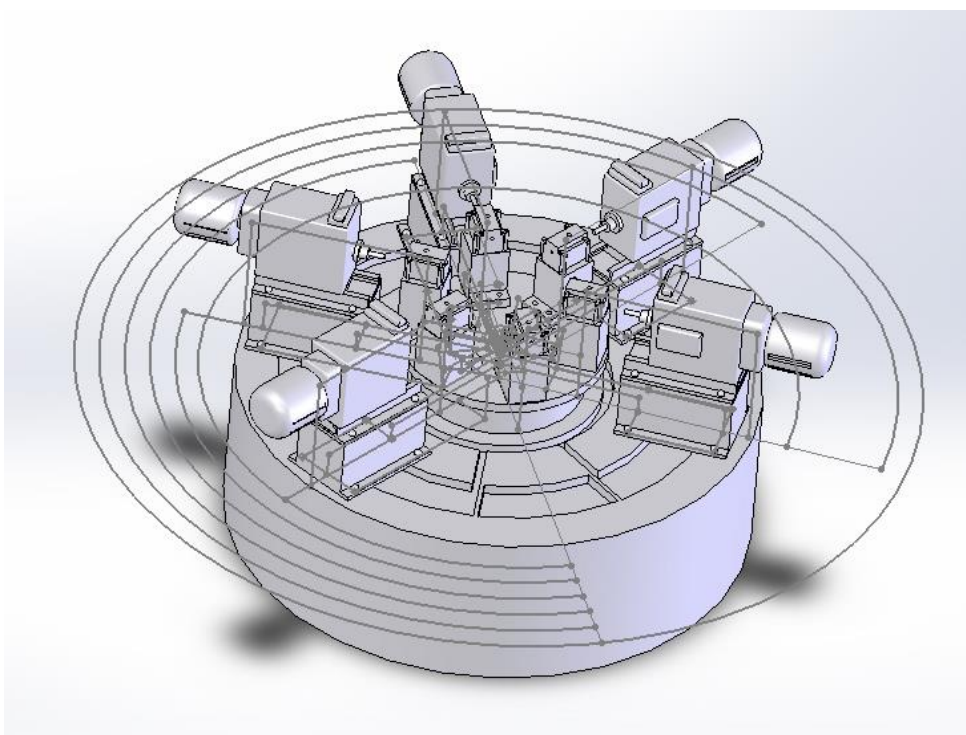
Монтаж елементів багатопозиційного агрегатного верстата на заздалегідь підготовлені бази
